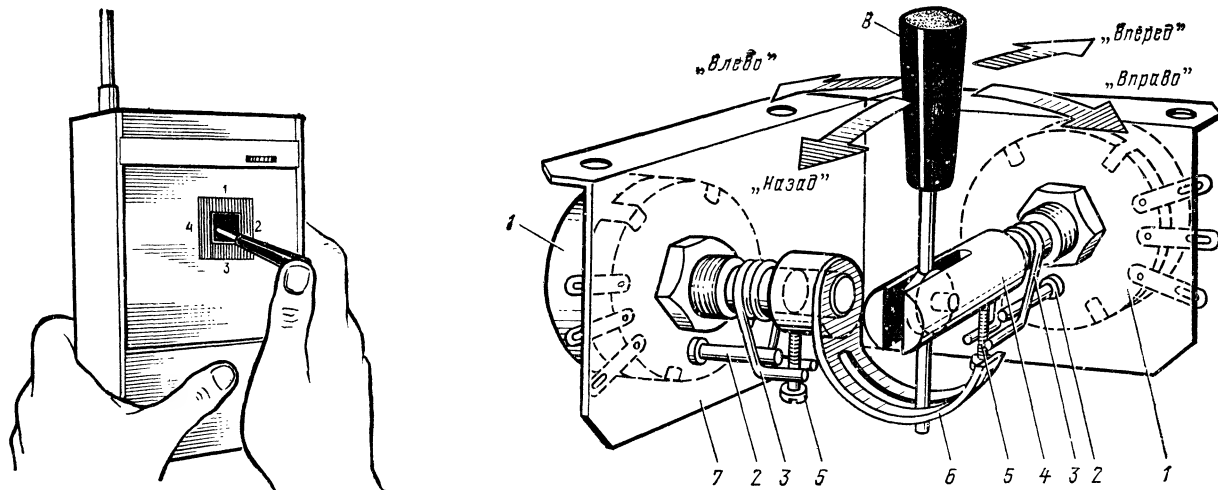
Внешний вид передатчика и конструкция механизма управления им.
